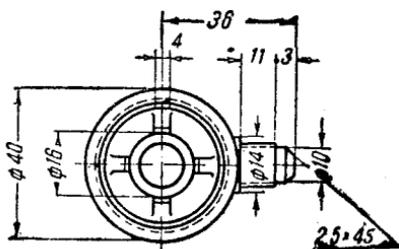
Дет. № 331. Корпус фильтра поплавковой камеры
